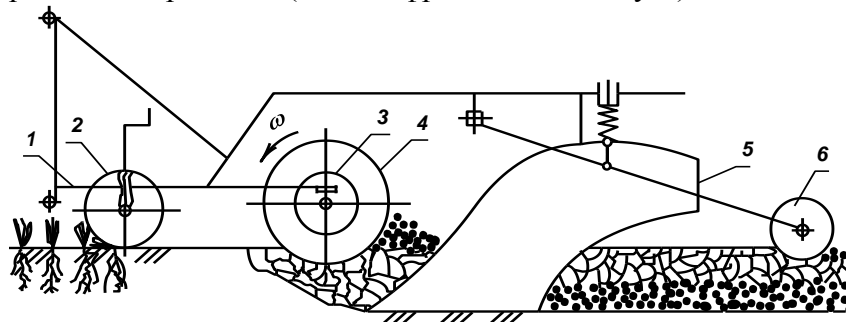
Схема пахотных агрегат для гладкой безбороздной вспашки с активными и пассивными рабочими органами.
